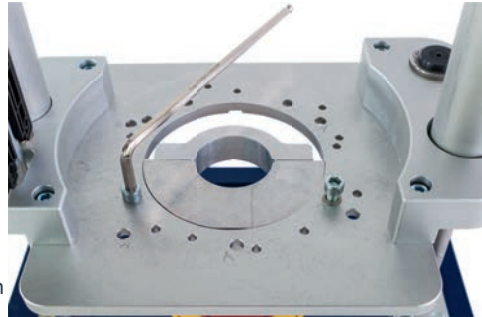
Sicht auf Befestigungsschrauben (OFL2.0 stellvertretend)
